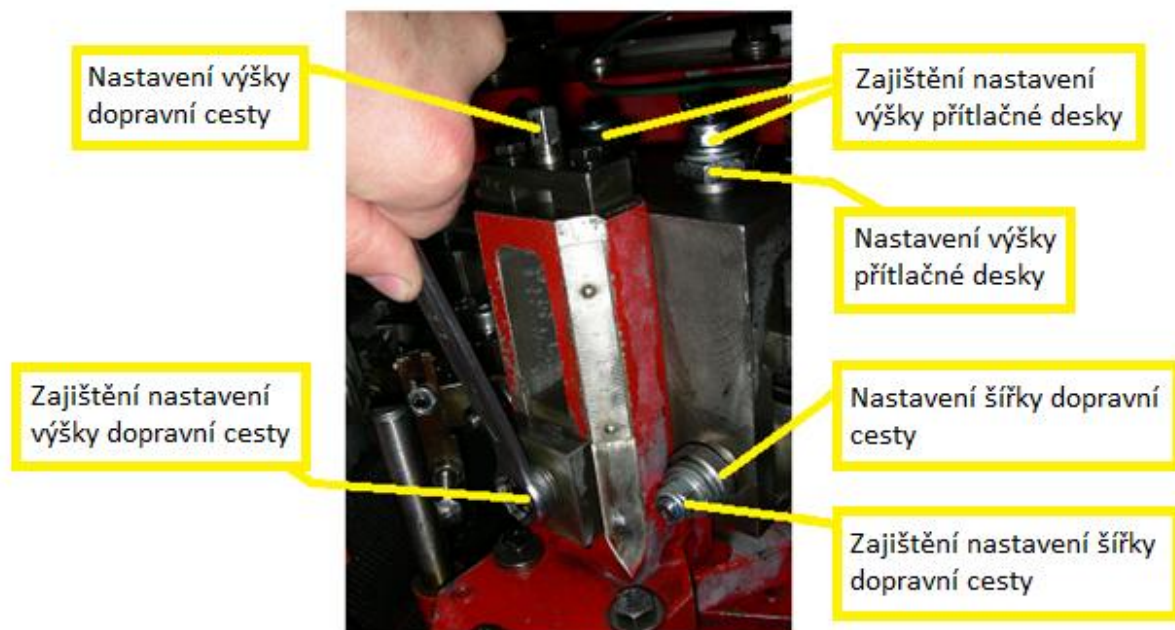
Montáž dopravních cest před válcovačkou [21]
